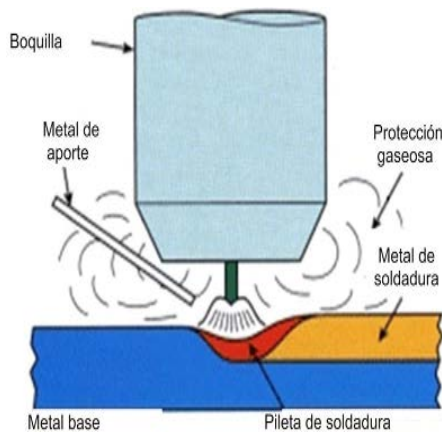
Soldadura en atmósfera inerte con electrodo de tungsteno.
